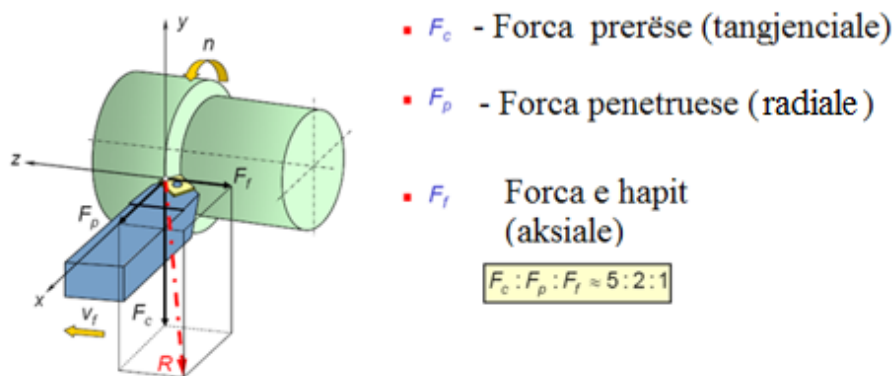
Komponentet kryesore të forcave të prerjes
